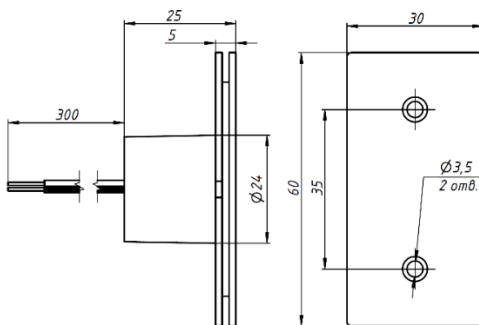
Габаритные и установочные размеры устройства передачи энергии (приемник и передатчик)
